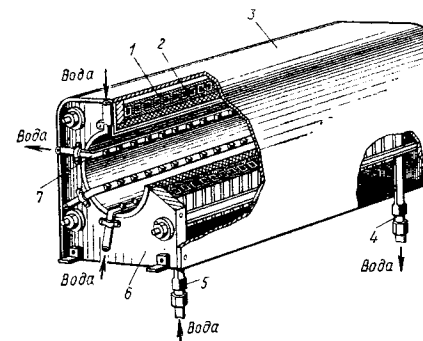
Индуктор для сквозного нагрева цилиндрических заготовок
